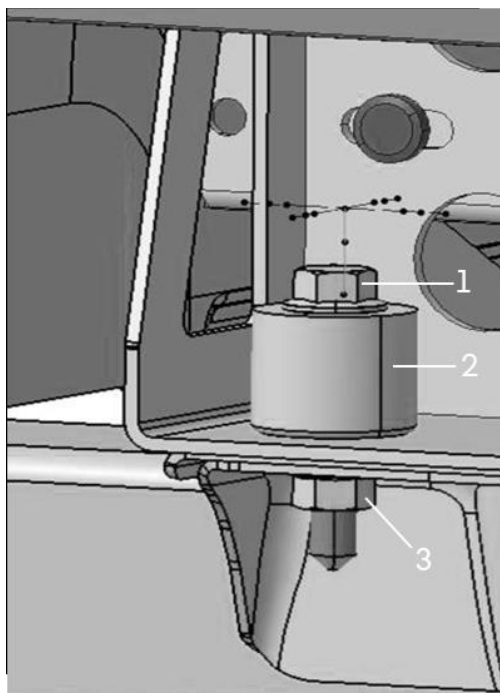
exemple de conception : assemblage vissé avec élément amortisseur (schéma de principe)
